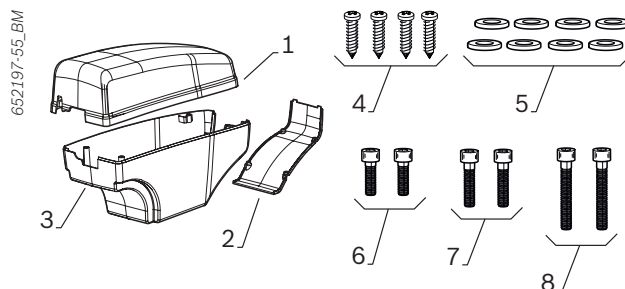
Accessoires pour le montage du recouvrement arrière de colonne
